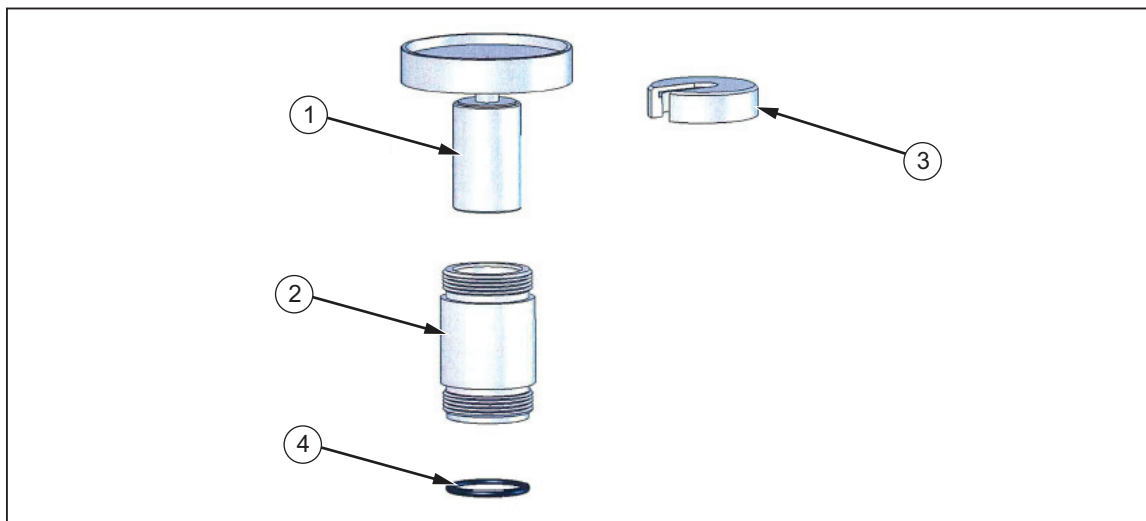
Сборочный чертеж поршневой пары - 22 мм
